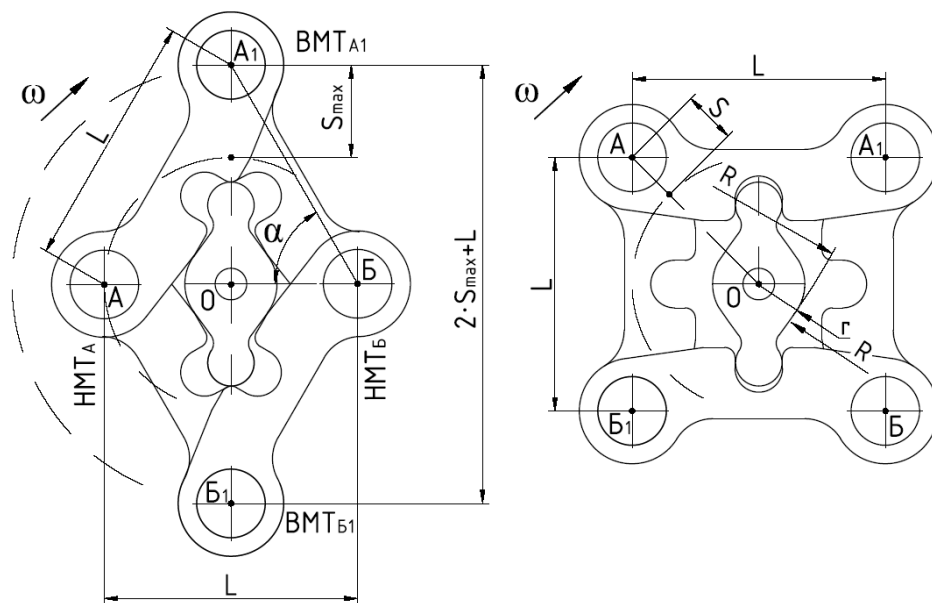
Загальна кінематична схема механізму руху роторно-поршневого двигуна нової конструкції
